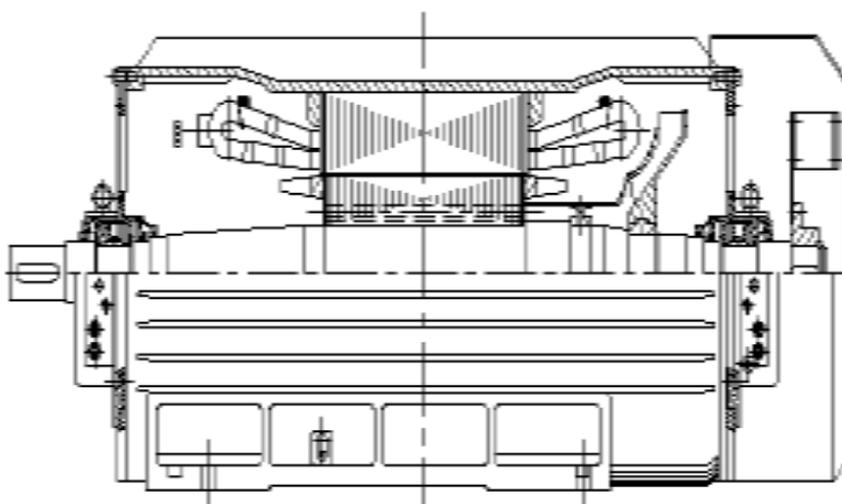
Сборочный чертеж двигателя с методом охлаждения IC411 и конструкцией подшипника скольжения
